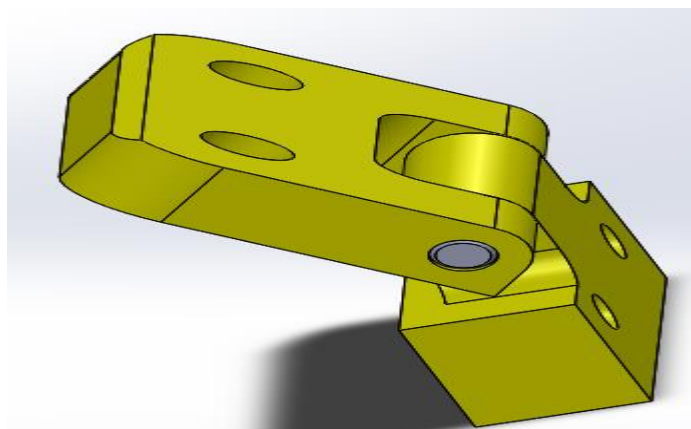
Porte pièce latérale conçue par SolidWorks.
